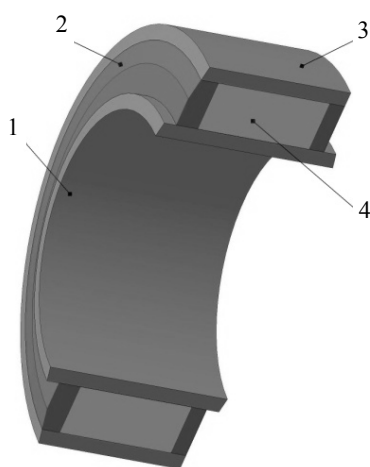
Конструкция сварного пустотозаполненного бандаж сварной конструкции для вращающейся печи
